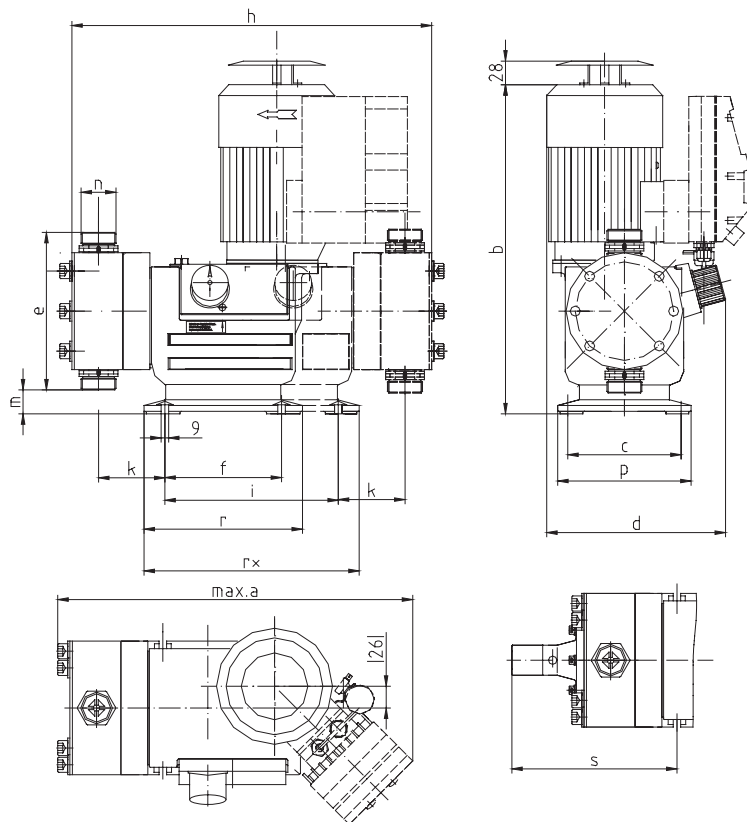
Габаритный чертёж DMX 226 (часть 2)
